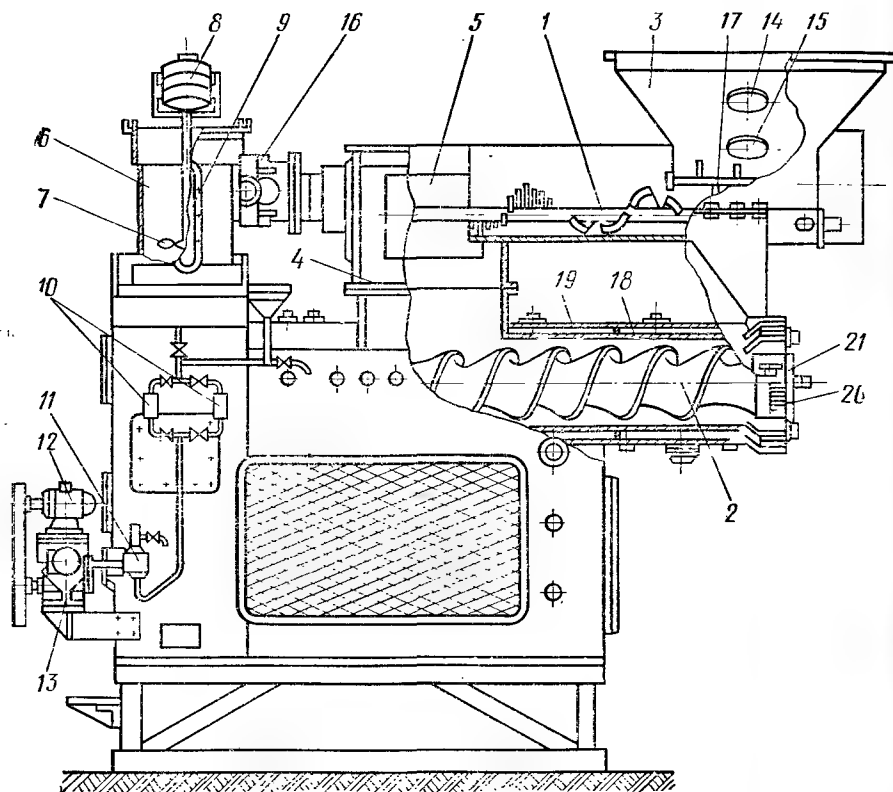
Двухступенчатый шнековый пресс-смеситель (разрез по рабочей камере).
